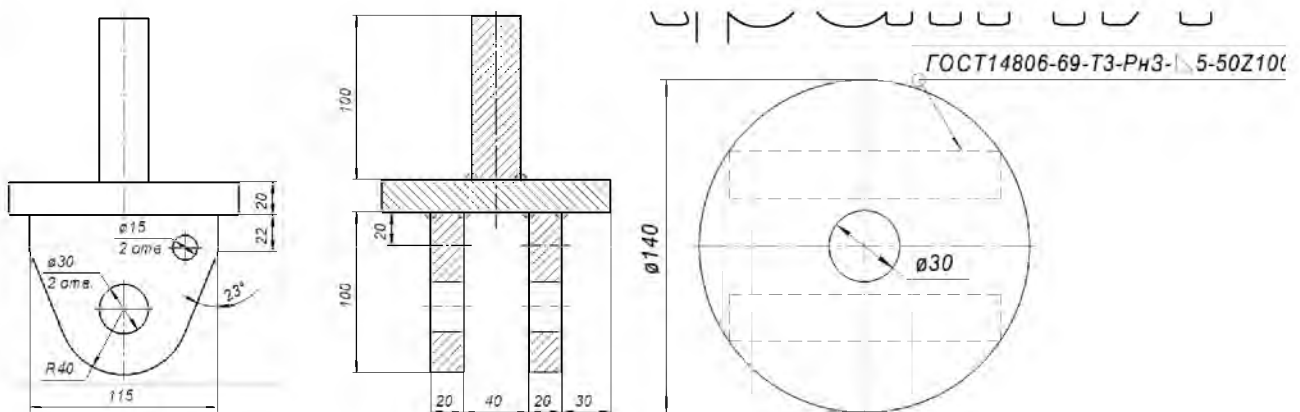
Корпус обертаючий для кріплення стійки до рами
